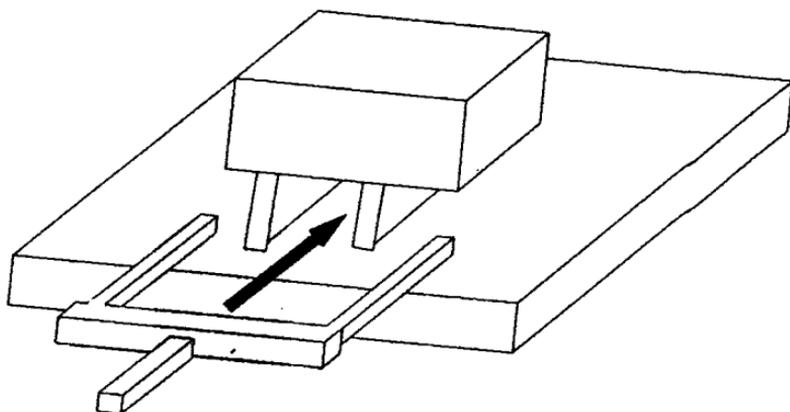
Поддерживающее захватное устройство вилочного типа
